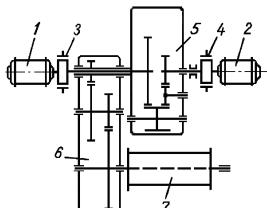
Кинематические схема многоскоростной электрореверсивной лебедки с планетарным редуктором: 1, 2 – электродвигатели; 3, 4 – тормоза; 5 – планетарный редуктор; 6 – двухступенчатый редуктор; 7 – барабан
